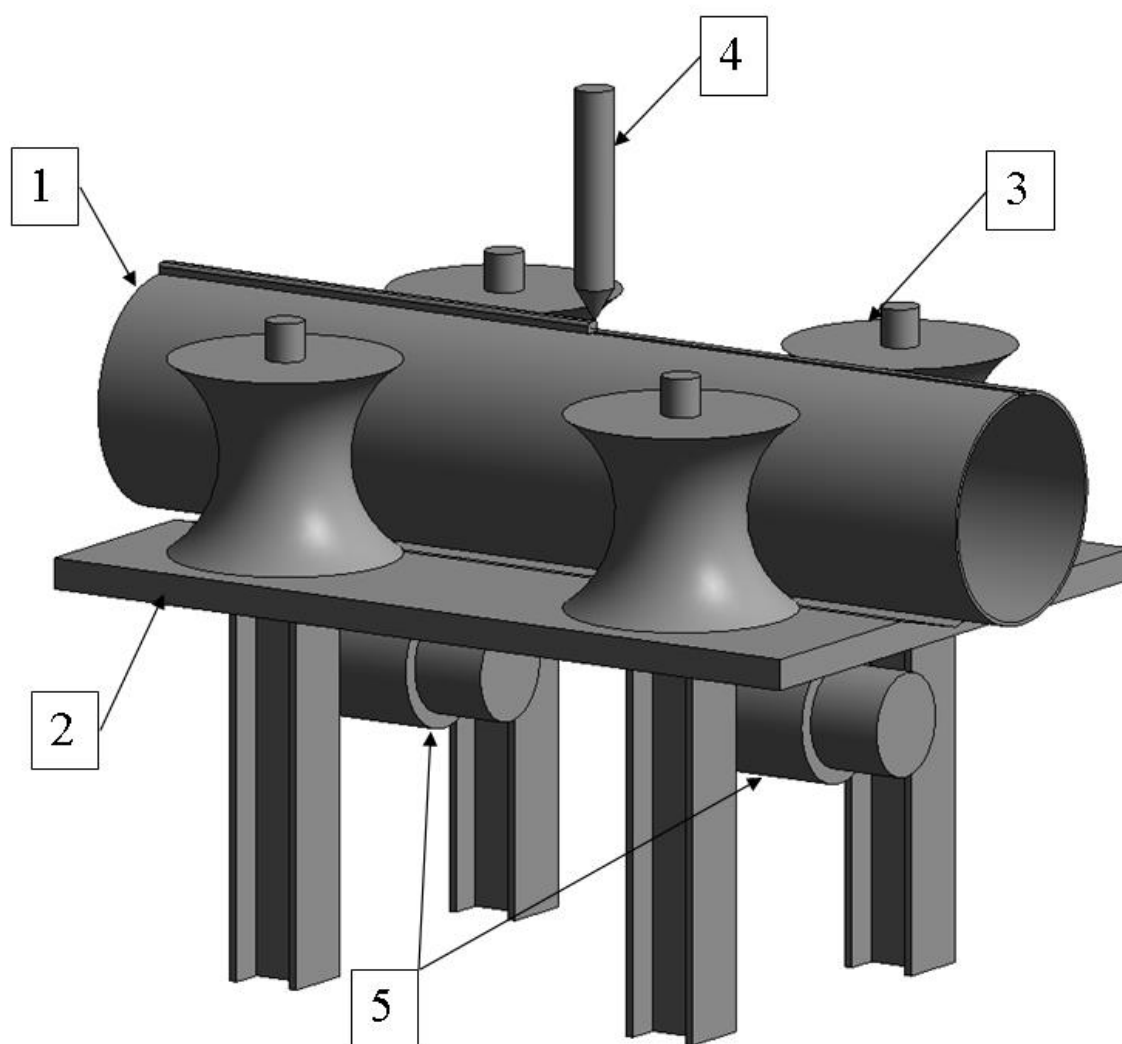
Схема виробництва зварних труб із застосуванням вібраційної обробки: 1 – трубна заготовка; 2 – еджерні кліті електрозварювальної машини, 3 – підтискні ролики, 4 – зварювальний агрегат, 5 – вібраційна установка.
